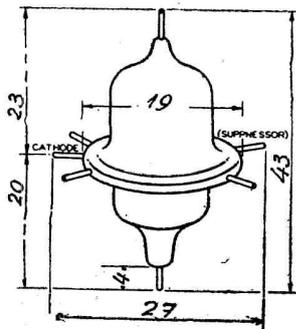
Silhouette et dimensions de la pentode "gland" 954
